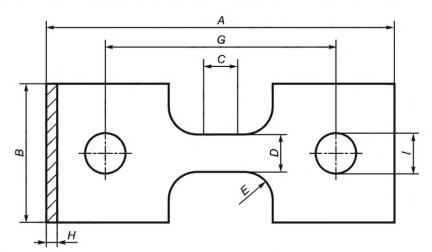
Образец для испытания типа В, полученный методом механической обработки для испытания при растяжении (для *e* ≥ 25 мм)
